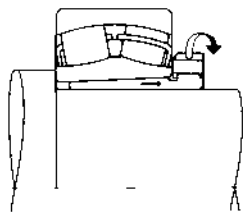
Удаление запрессовыванной втулки с помощью гайки (1)
